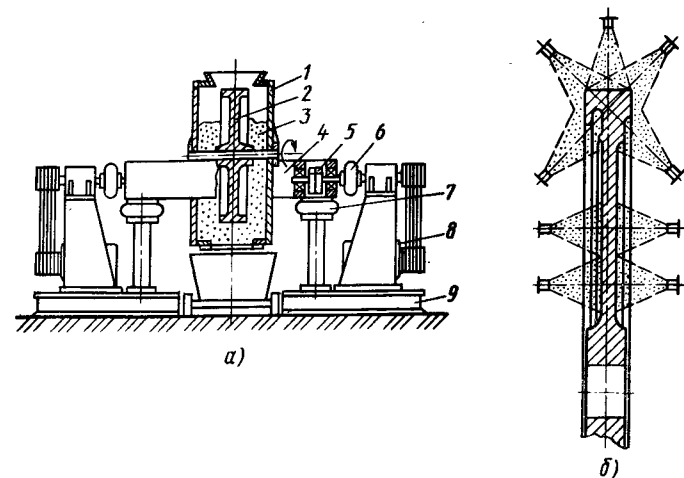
Схемы деформационного упрочнения дисков турбины и компрессора: а — виброупрочнение на установке ВУД-1000ДМ; б — струйно-гидравлическое упрочнение; 1 — контейнер; 2 — обрабатываемый диск; 3 — рабочая среда; 4 — подвижная рама; 5 — вибратор; 6, 7 — упругие элементы; 8 — электродвигатель; 9 — основание
